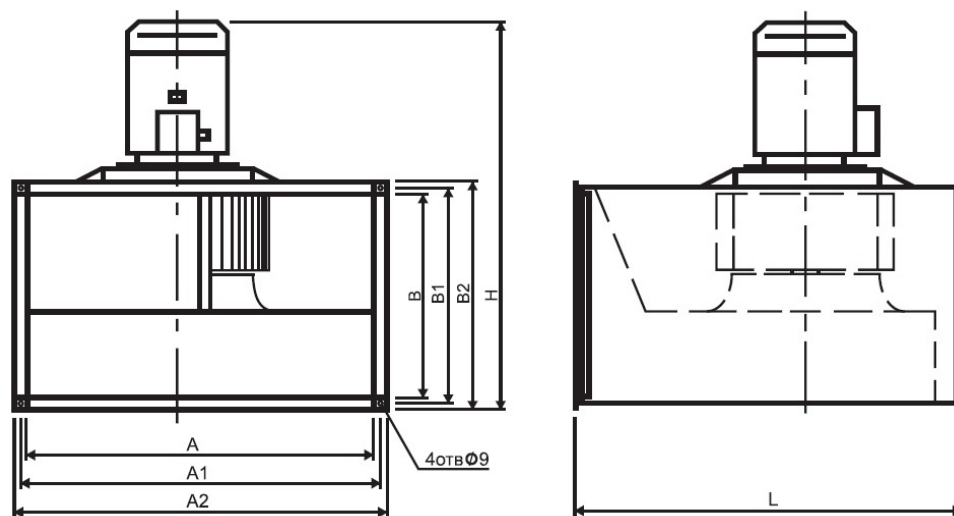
Габаритно-присоединительные размеры ВКПН-В.
